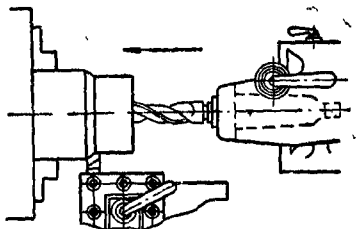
Схема совмещения обработки отверстия и наружной цилиндрической поверхности.
